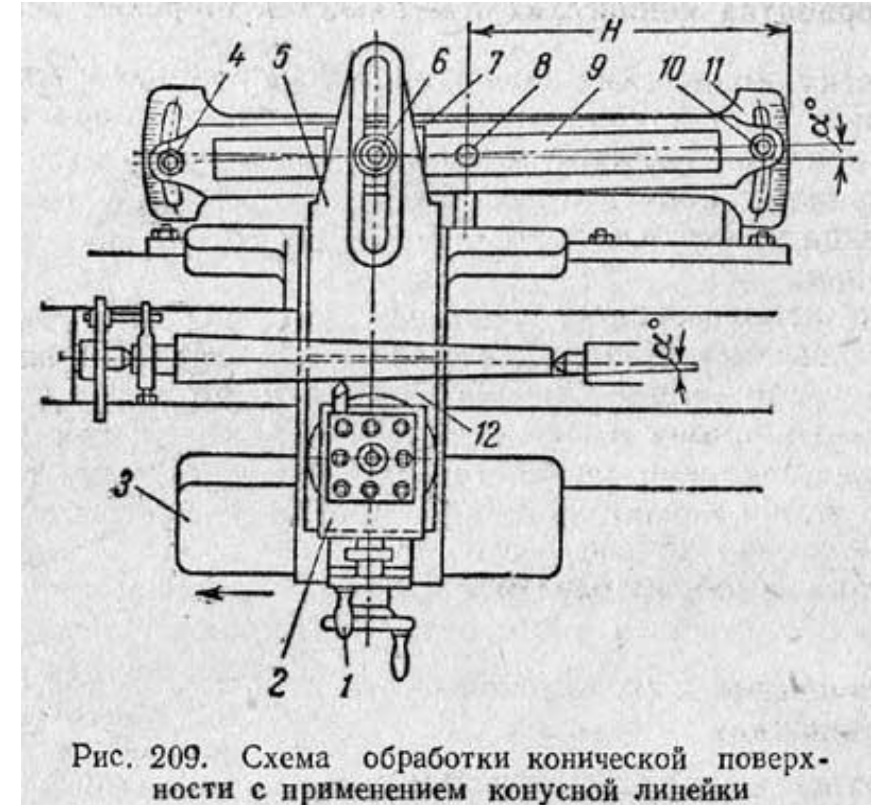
Схема обработки конической поверхности с применением конусной линейки
